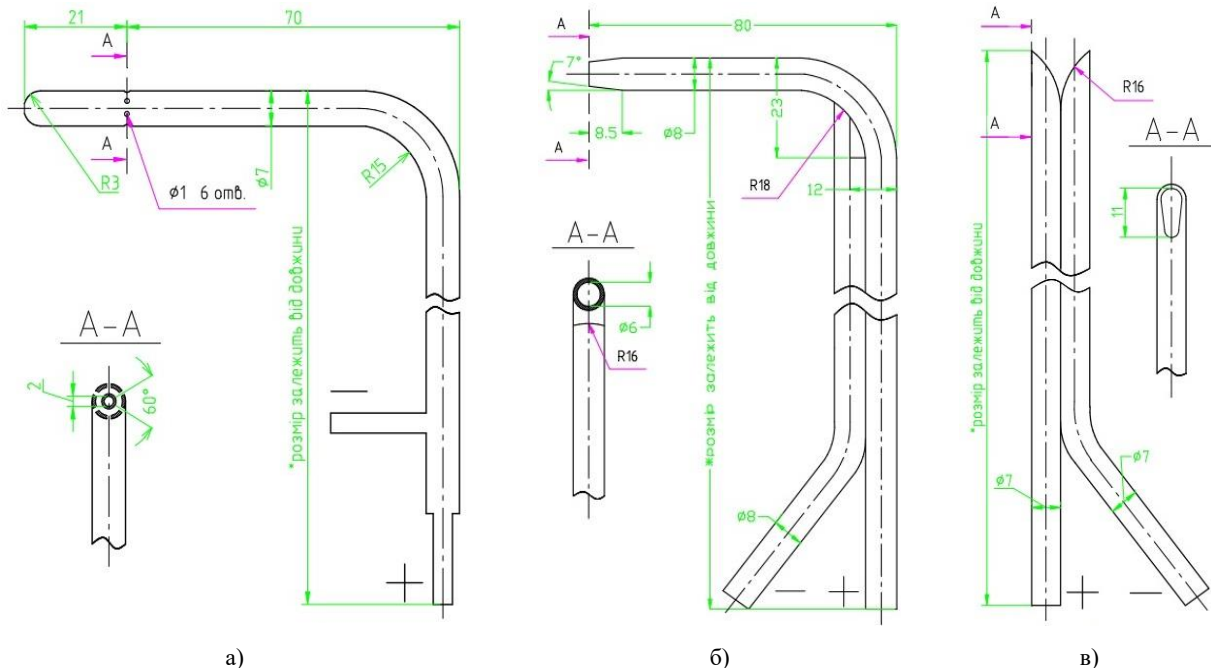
Напірні трубки для точкового вимірювання швидкості газових потоків - а) конструкція Піто, б) конструкція НІОГАЗ, в) конструкція Проба
